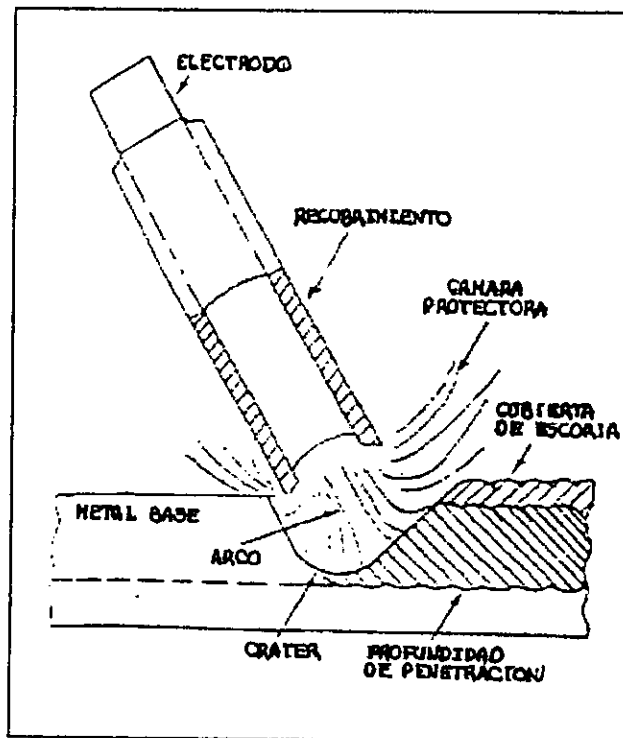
soldadura de arco con electrodo revestido.
